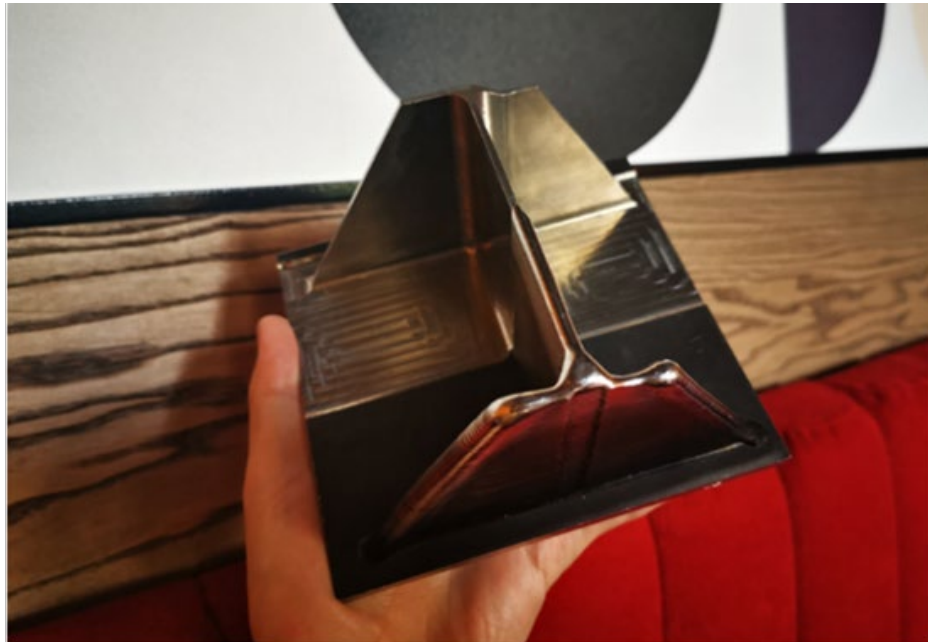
Авіаційна деталь до та після механічної обробки, виготовлена за допомогою X-Beam 3D Metal Printing
